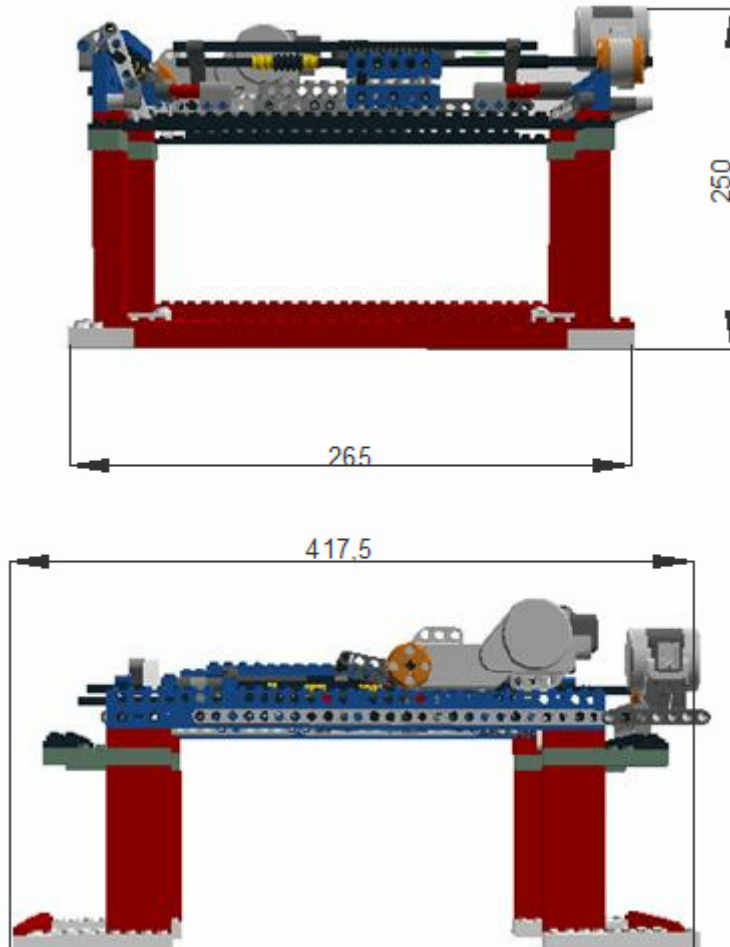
B.B3 ): Dimensiones quinto montaje.
